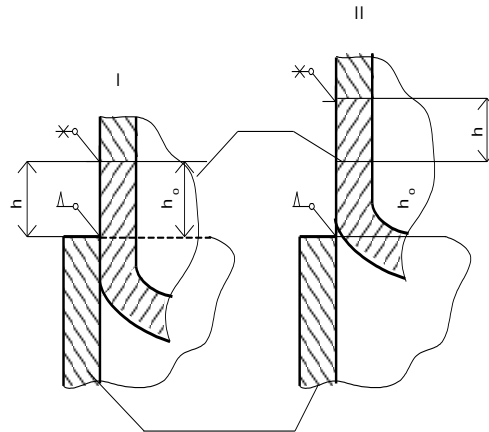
Способы соединения опоры с корпусом аппарата:
